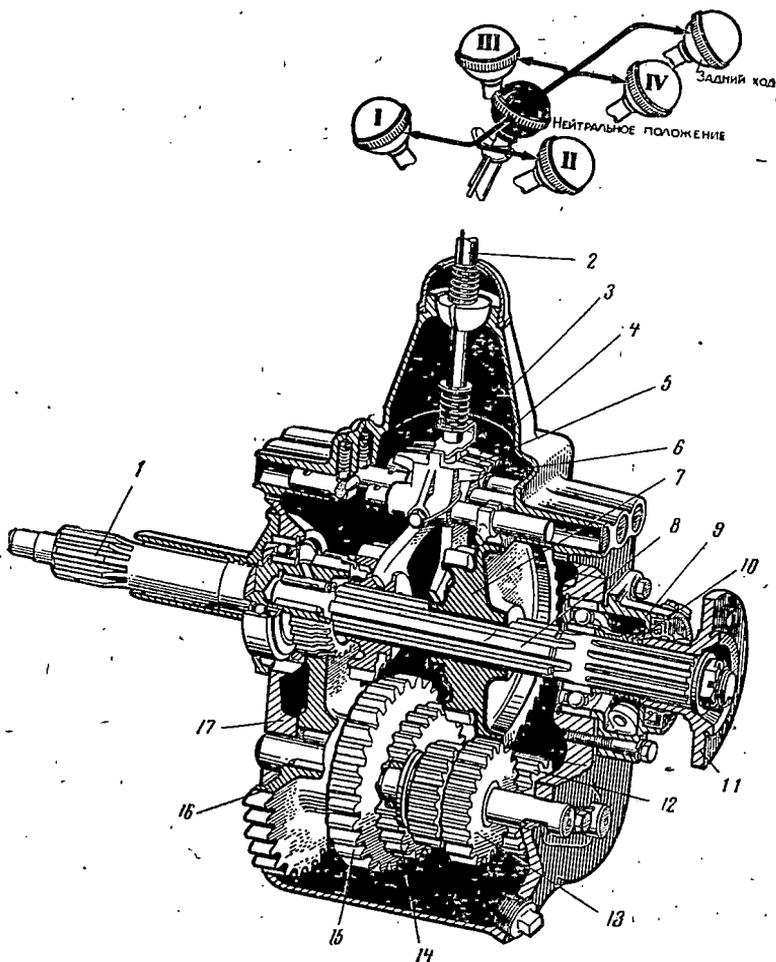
Коробка передач автомобиля ГАЗ-51А:
